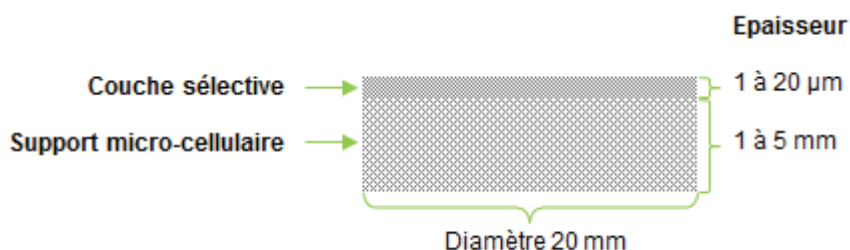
Dimension des pièces poreuses de type SiBC à réaliser
